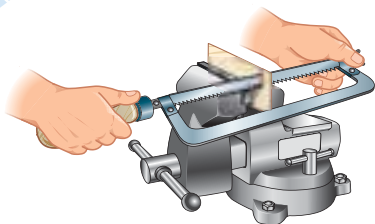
Резание металла с поворотом ножовочного полотна
